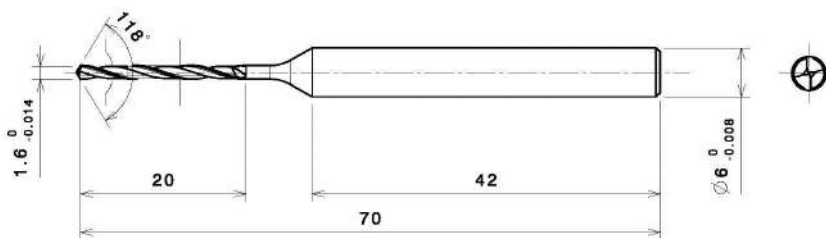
Креслення твердосплавної фрези SSD D1.6X20FX 70-6 із сплаву UF10
